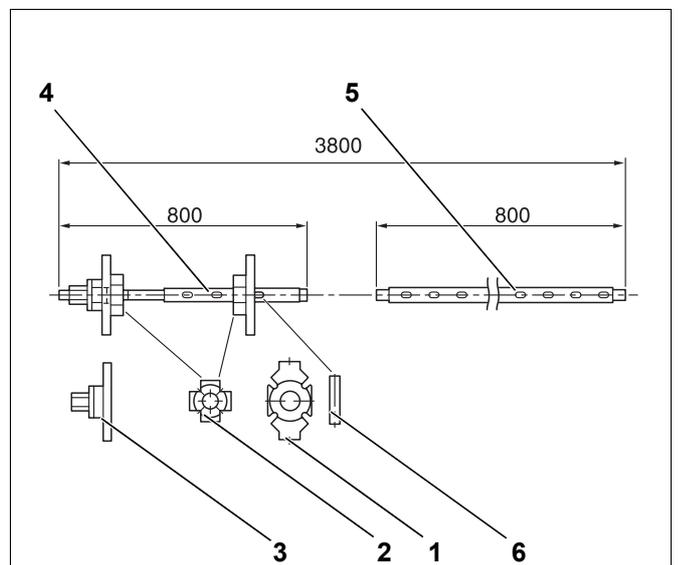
Kesselpresswerkzeug Größe 2.3 (Maße in mm)
